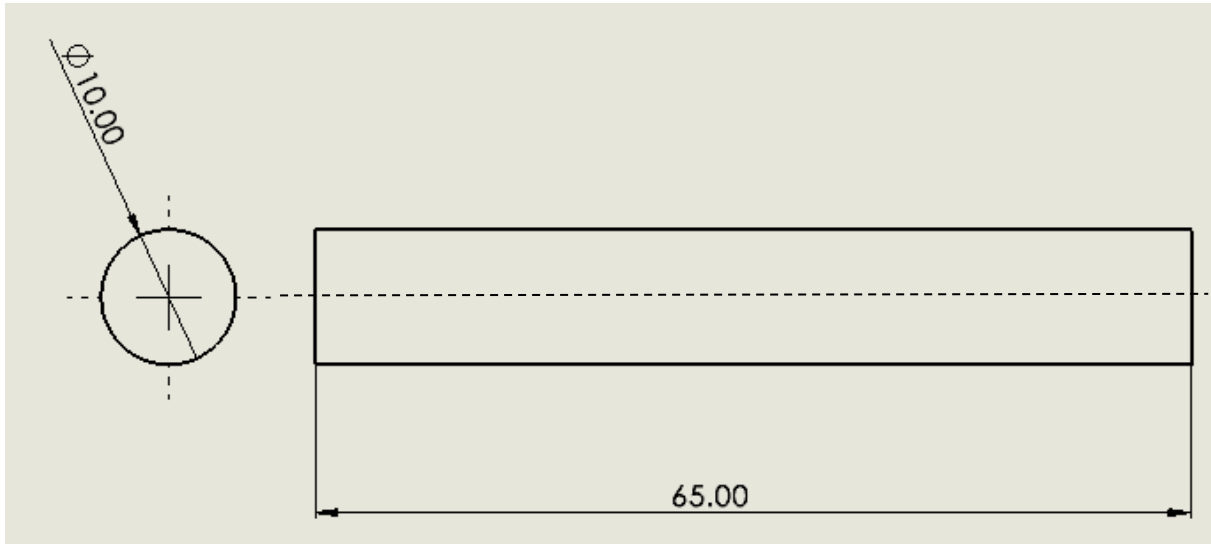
Dimensionamiento de muestras para soldar mediante FSW.
